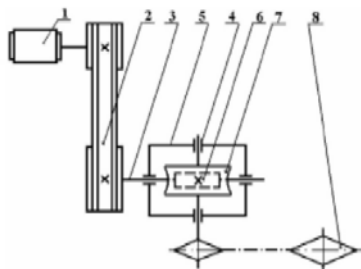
Кинематическая схема привода с червячным редуктором
